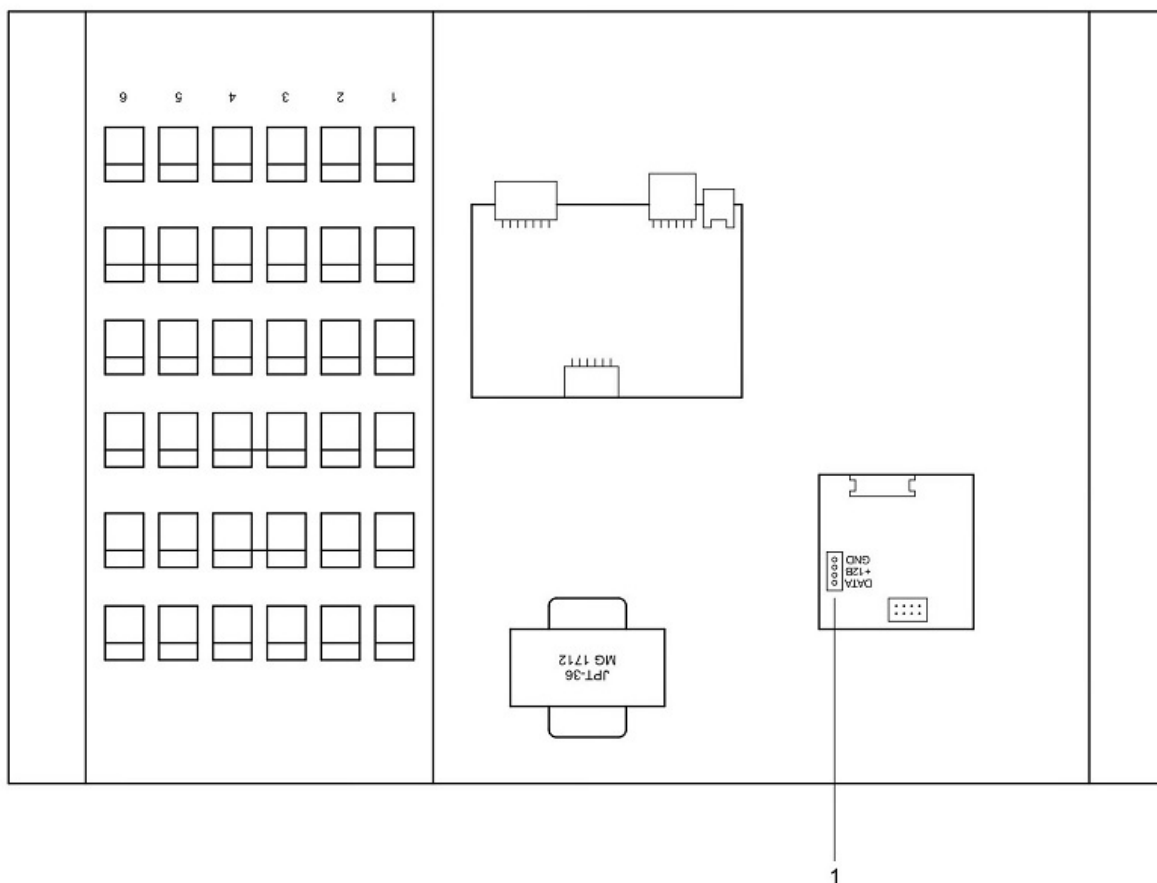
Вид пульта с поднятыми частями передней стороны корпуса
